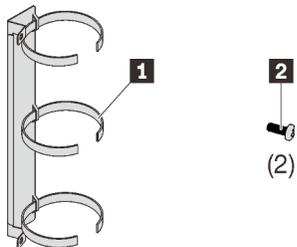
Componentes do suporte de gerenciamento de cabos frontais 6U
